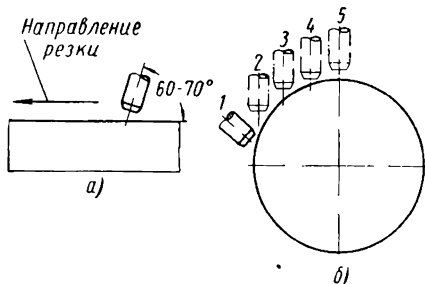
Положение резака в процессе резки металла: а — полосового; б — круглого сечения
